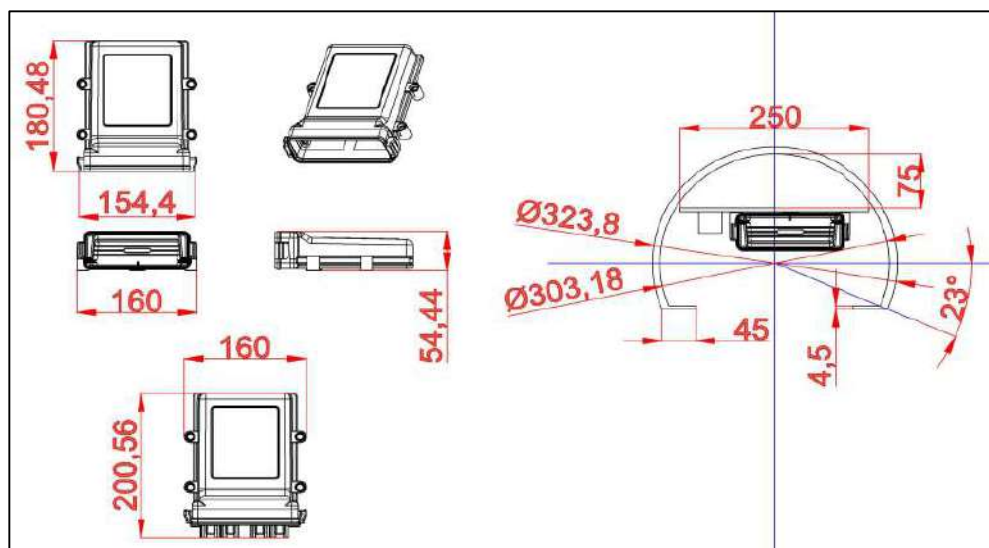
Vista de Planta Controlador DiverBiss, instalación propuesta dentro de poste de monitoreo remoto
